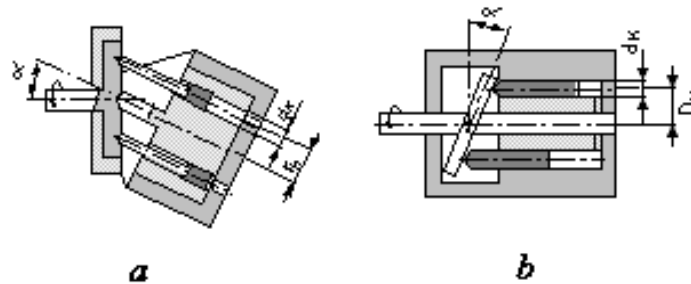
Motor hidráulico de pistões axiais:(a) tipo eixo inclinado, (b) tipo disco inclinado.
